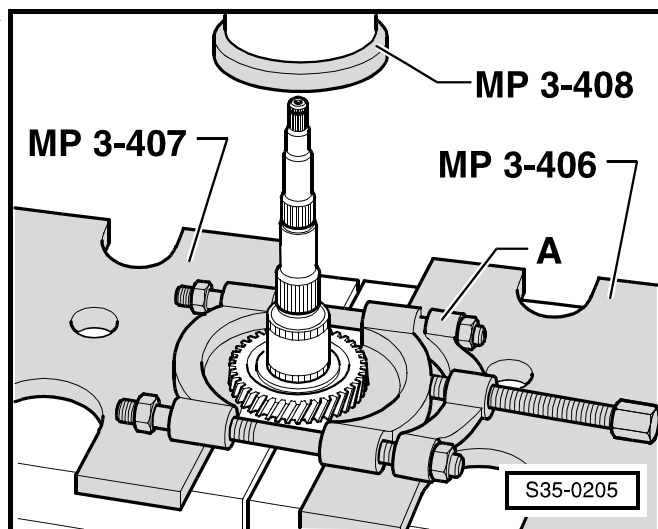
Выпрессовывание скользящей муфты с кареткой синхронизатора 3-ей и 4-ой передач ►
